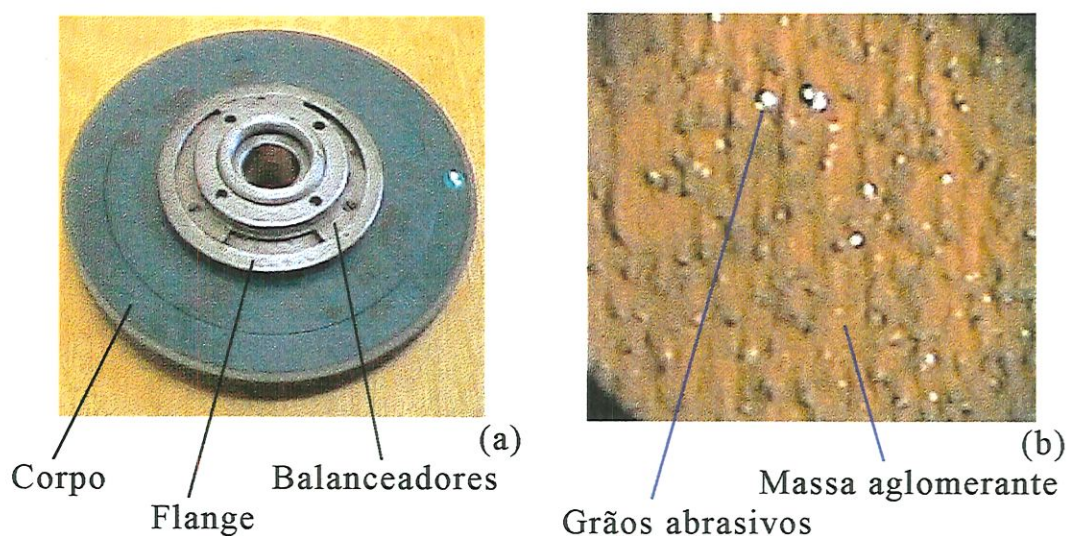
Rebolo de diamante (a) e superfície de corte (b)
